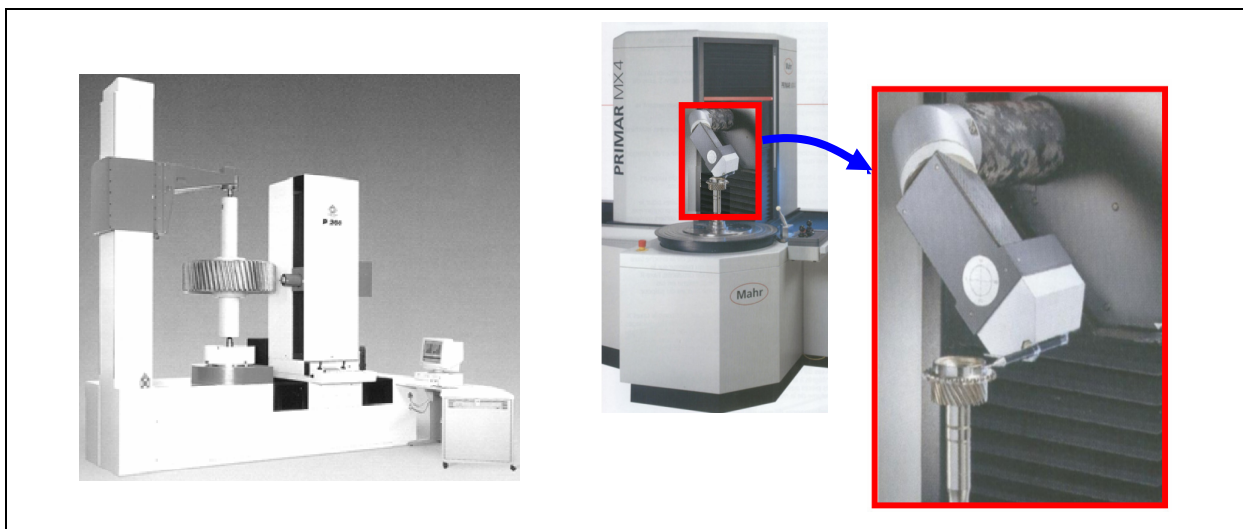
Machines de contrôle spécifiques pour les engrenages [MAH01].
